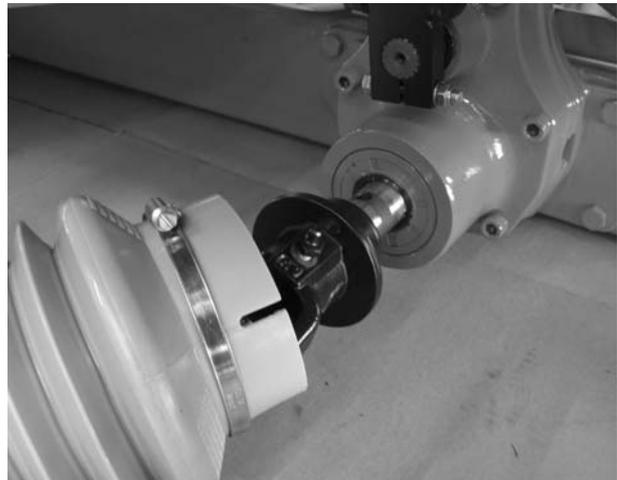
Gelenkwelle auf Getriebezapfen aufstecken
